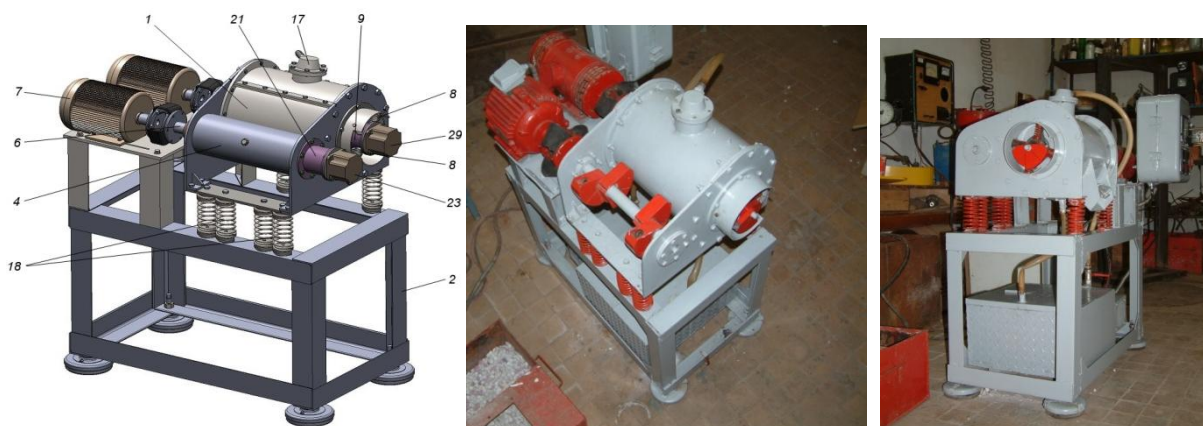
Пристрій для вібраційно-абразивно-зміцнювальної обробки деталей
